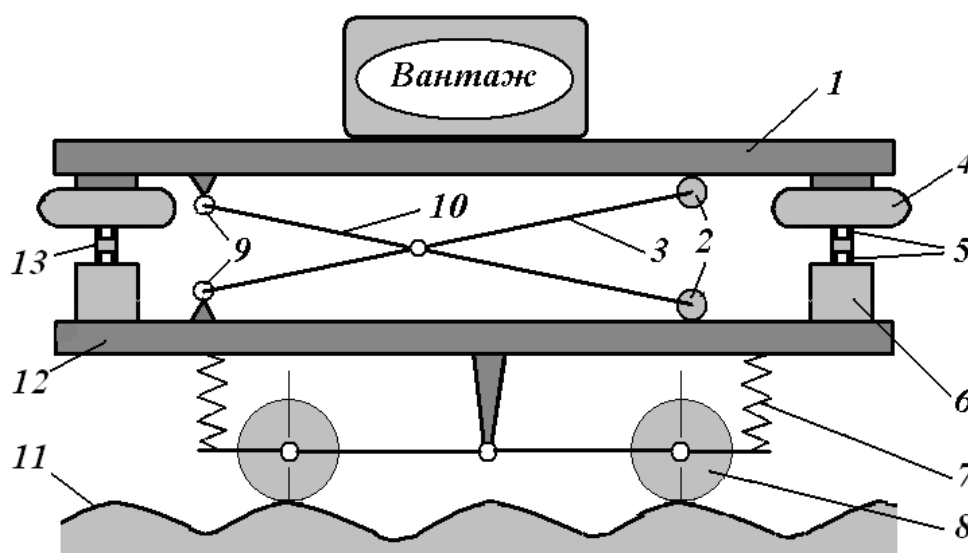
Схема конструкции транспортного средства для перевозки опасных грузов 1 - грузовая платформа, 2 - опорные катки, 3, 10 - рычаги направляющего параллелограмма, 4 - резинокордная однофровая оболочка, 5 - дроссельная шайба, 6 - дополнительный резервуар, 7 - пружины первой ступени подвешивания, 8 - колеса тележки, 9 - шарнирные крепления рычагов направляющего параллелограмма, 11 - профиль дороги, 12 - опорная платформа, 13 - воздушный трубопровод.
